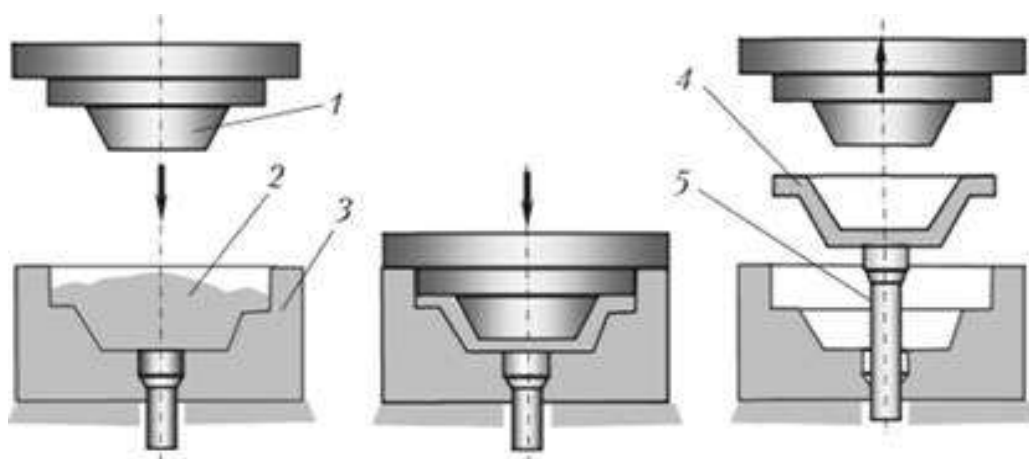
Схема прямого пресування заготовок з пластмас:
